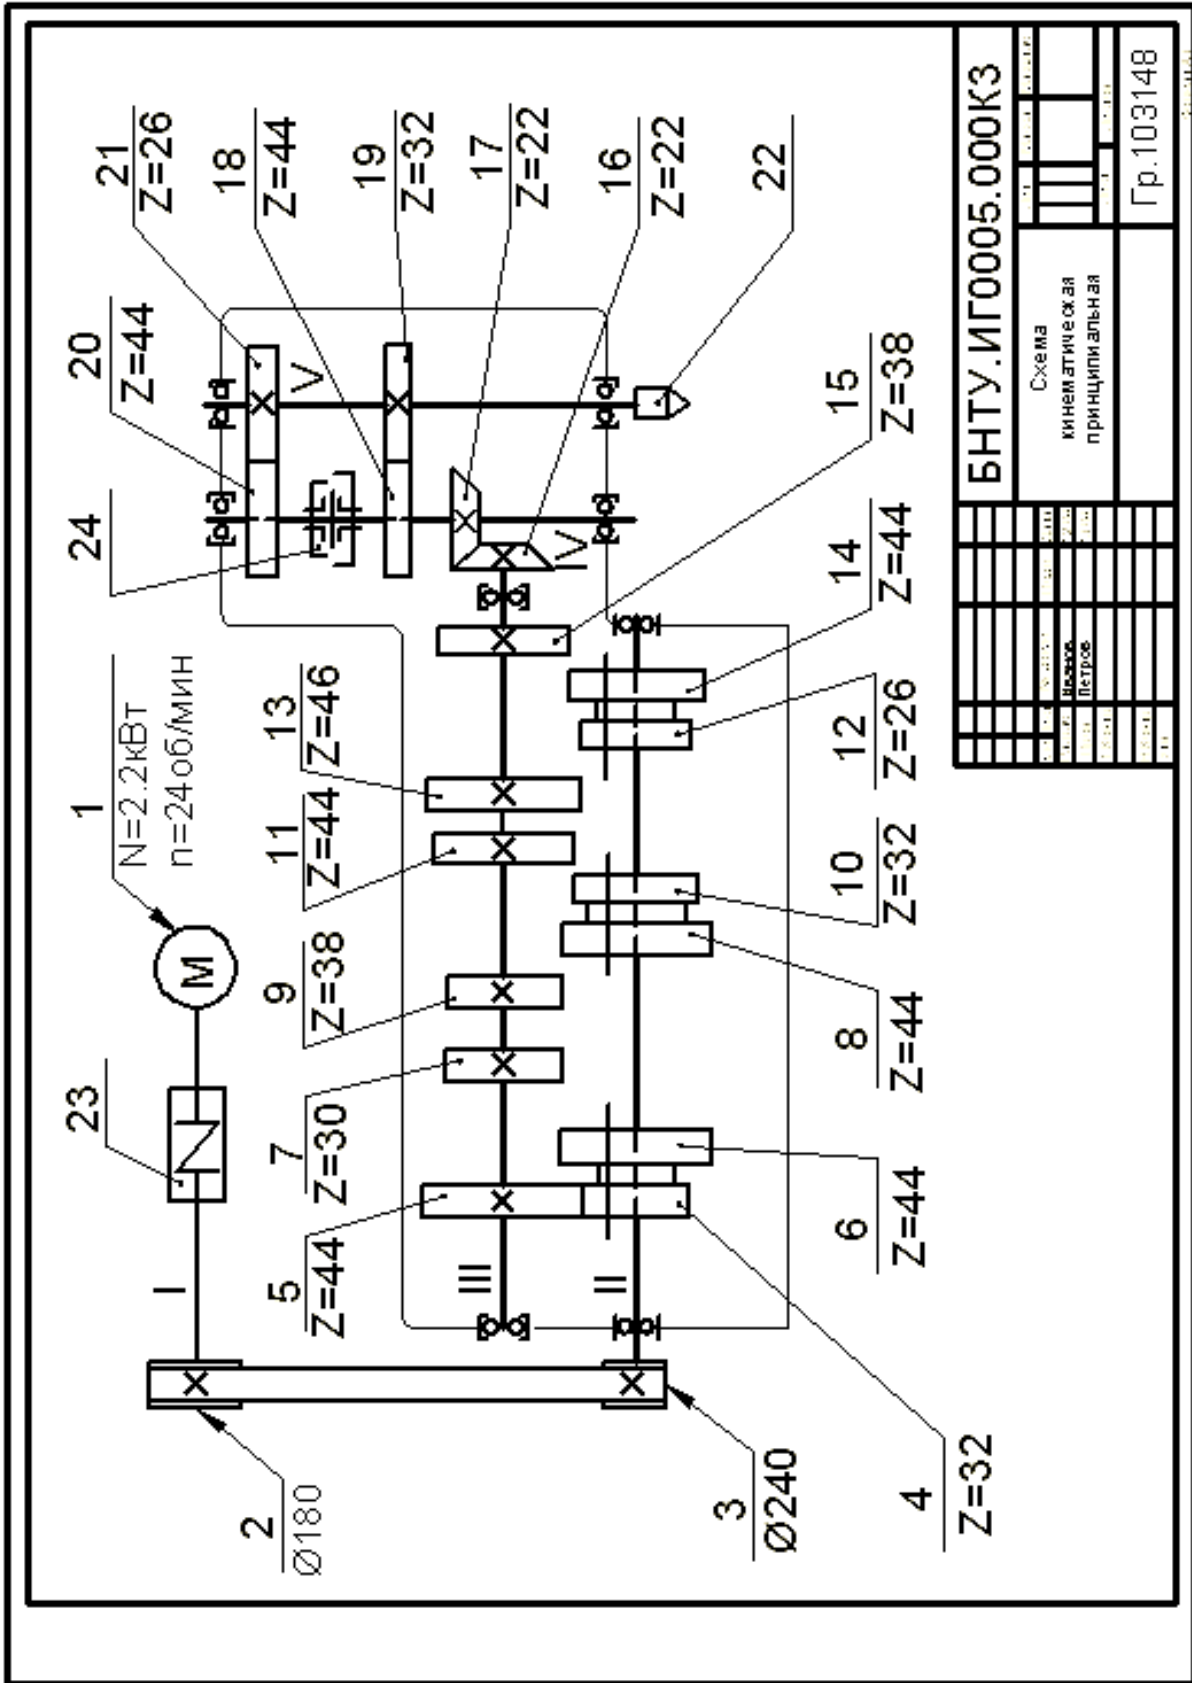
Коробка скоростей шпинделя вертикально-фрезерного станка (образец выполнения графической работы)
